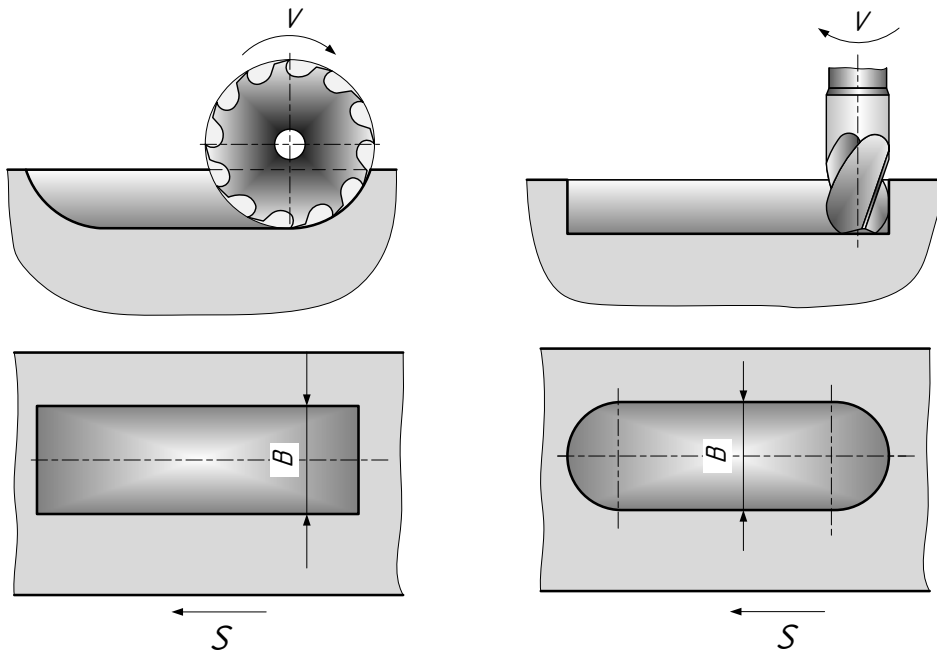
Обработка шпоночного паза дисковой и концевой фрезой
